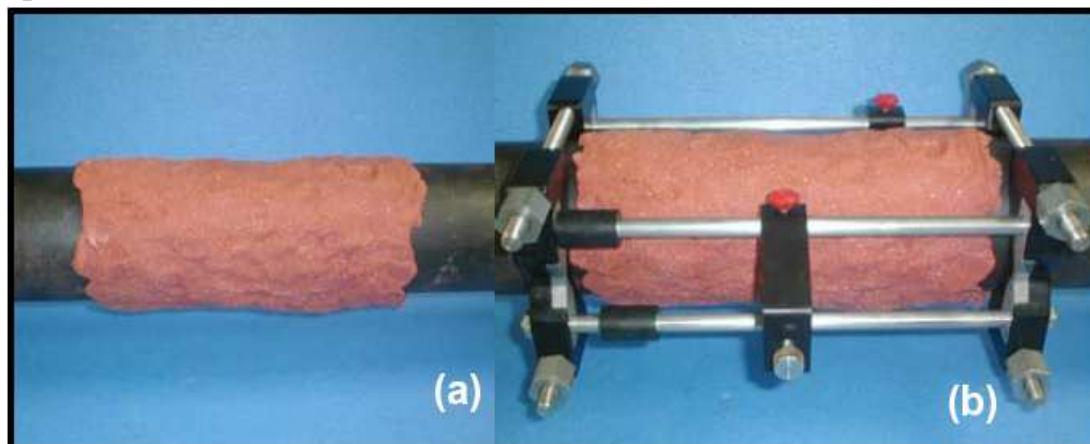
Распределение материала DMP-3 (a) и повторная установка зажимного приспособления (b)
